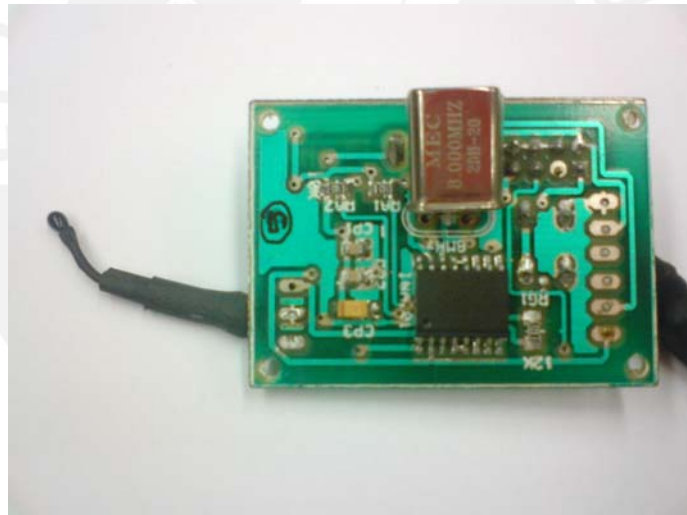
Imagen Tarjeta impresa de la Unidad de sensado - Lado reverso
